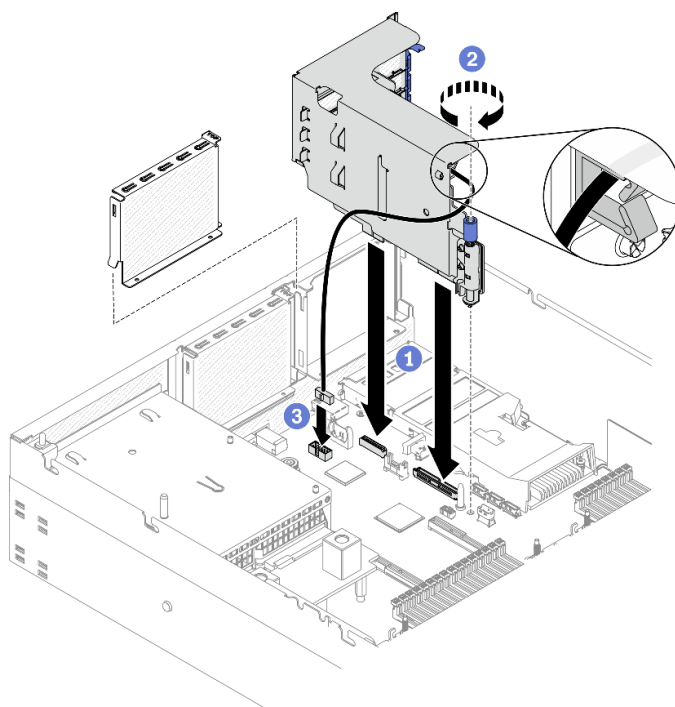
Установка платы-адаптера Riser PCIe 1 с установленным последовательным портом
